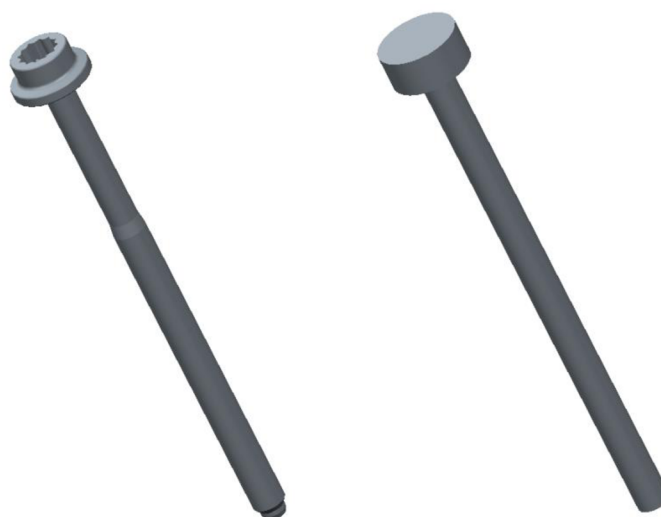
Model hlavy motoru před (vlevo) a po úpravách (vpravo)
